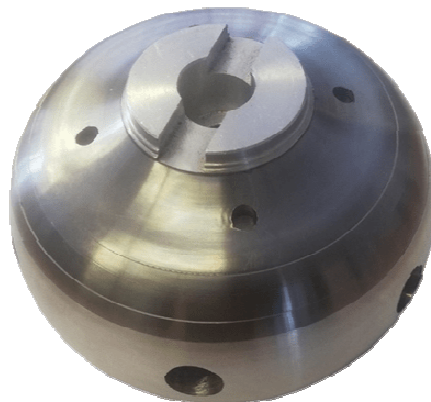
Опытный образец БМТФ с механизмом балансировки
